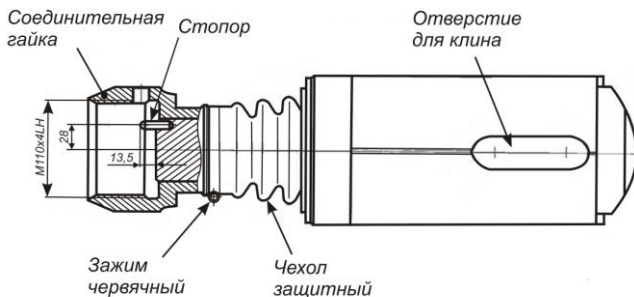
Шарнирный узел для БСУ-3 с монолитным корпусом сцепки
